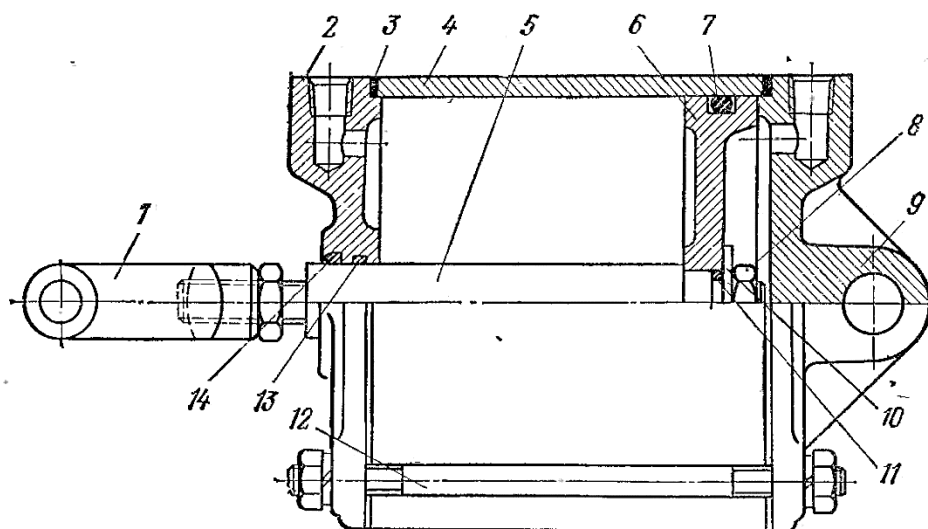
Пневмоцилиндр: 1 – вилка штока; 2 – крышка; 3 – про-кладка; 4 – корпус; 5 – шток; 6 – поршень; 7 – кольцо уплот-нительное поршня; 8 – гайка; 9 – крышка опорная; 10 – шайба; 11 – кольцо; 12 – шпилька стяжная; 13 – кольцо уплотнительное штока; 14 – кольцо грязезащитное
